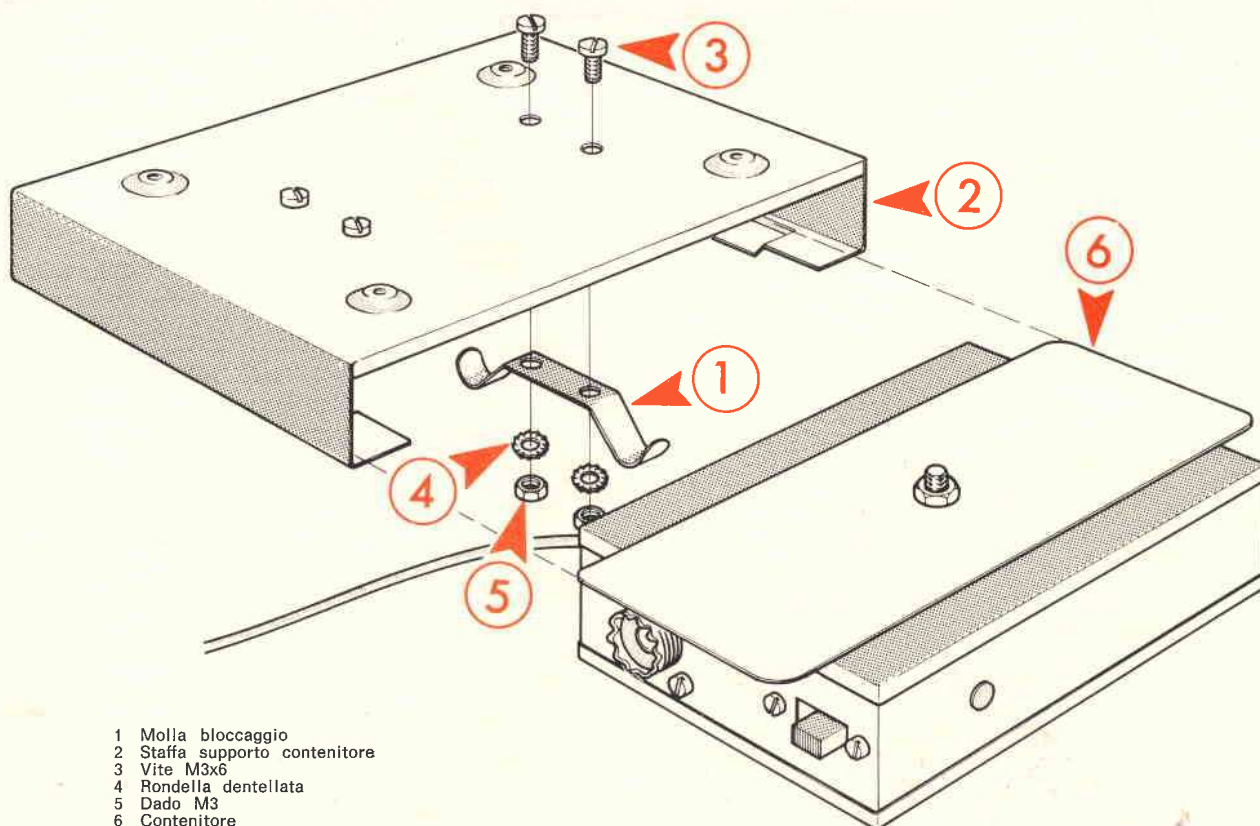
Montaggio del supporto per l'attacco in auto.
